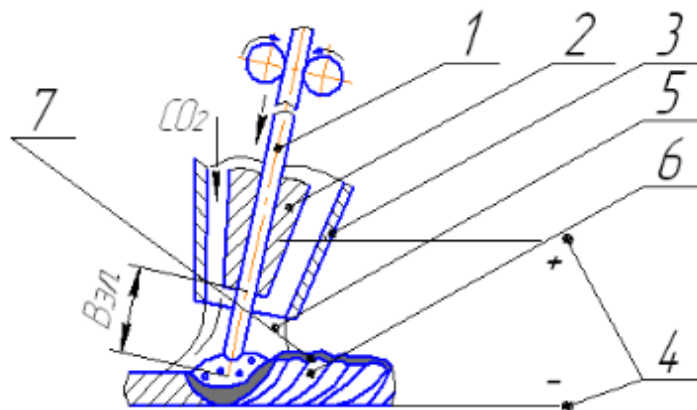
Схема образования сварного шва при сварке в среде углекислого газа:
